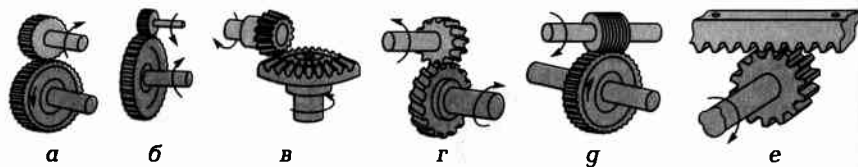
Виды зубчатых зацеплений (а—е)
